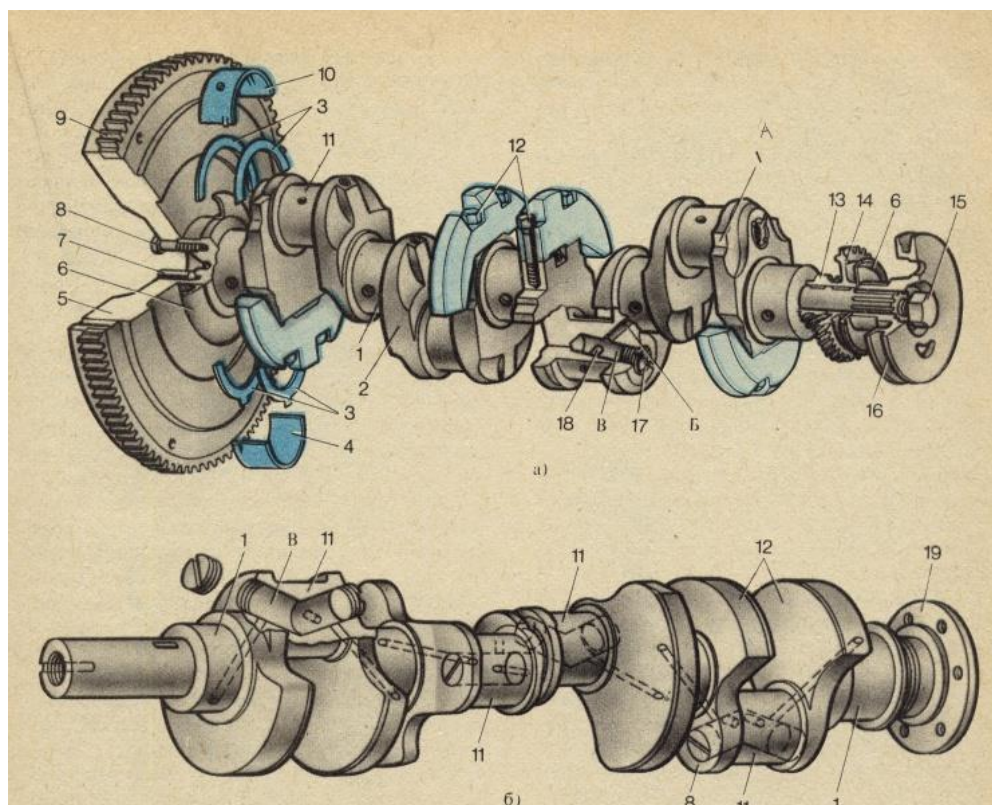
Конструкции коленчатых валов: а - дизельного рядного двигателя, б - V-образного двигателя; 1 - коренная шейка, 2 - щека, 3 - упорные полукольца, 4 - нижний вкладыш коренного подшипника, 5 - маховик, 6 - маслоотражатель, 7 - установочный штифт, 8 - болт крепления маховика, 9 - зубчатый венец, 10 - верхний вкладыш коренного подшипника, 11 - шатунная шейка, 12 - противовесы, 13 - шестерня коленчатого вала, 14 - ведущая шестерня привода масляного насоса, 15 - болт, 16 - шкив, 17 - пробка, 18 - канал для подвода масла, 19 - фланец; А - место клеймения размерной группы шеек коленчатого вала, Б - канал подвода масла в полость шатунной шейки, В - полость шатунной шейки
